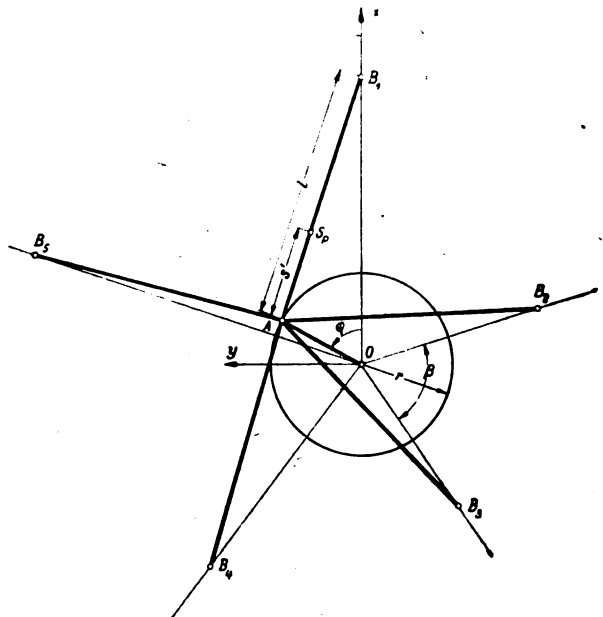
Sternmotor mit unmittelbarer Pleuelanlenkung.
